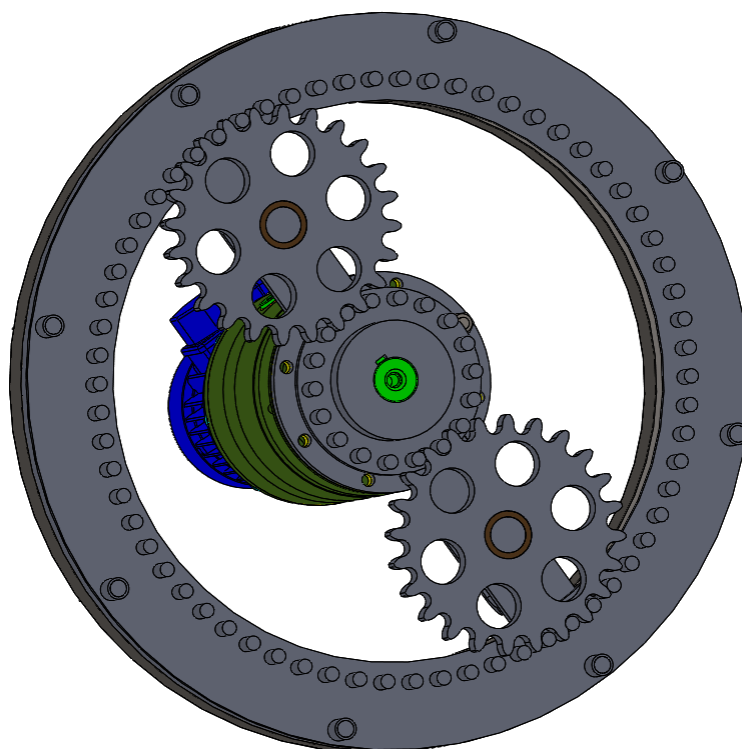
Цевочная передача с двумя промежуточными звездочками
